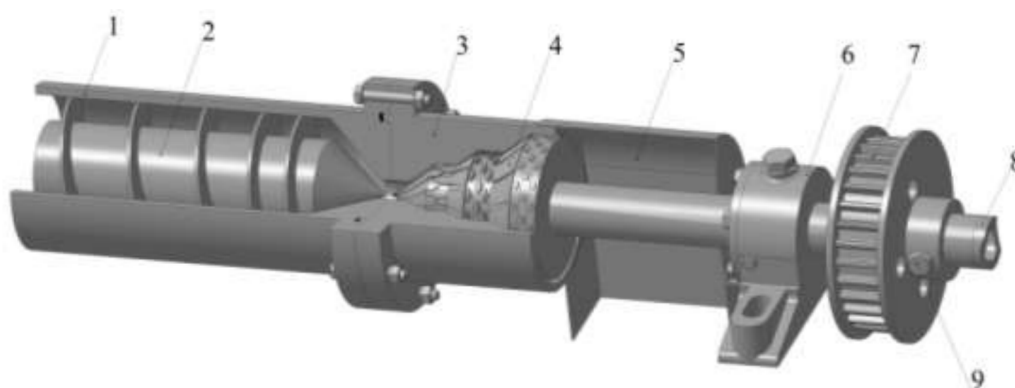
Екструдер: 1 - корпус шнека; 2 - шнек; 3 - формуюча головка; 4 - дорн; 5 - розвантажувальна камера; 6 - підшипникова опора; 7 - шків; 8 - копір; 9 - стопорний болт
